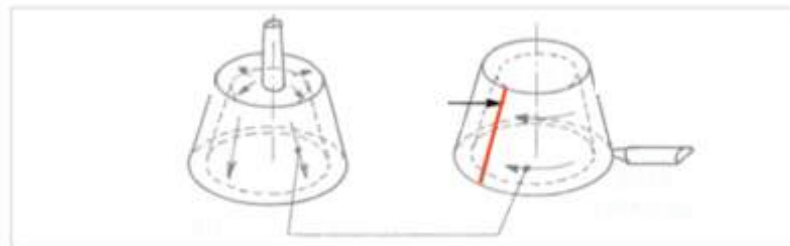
Llenado del molde y líneas de soldadura. Fuente: ECL
